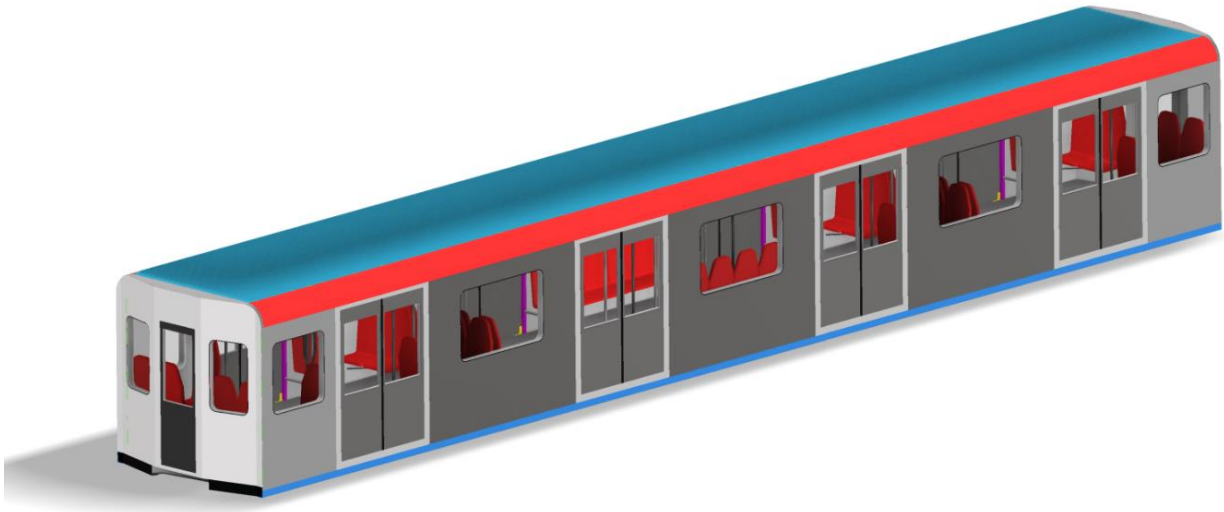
CAD vizualizace vytvořeného modelu diferenciální stavby metra
